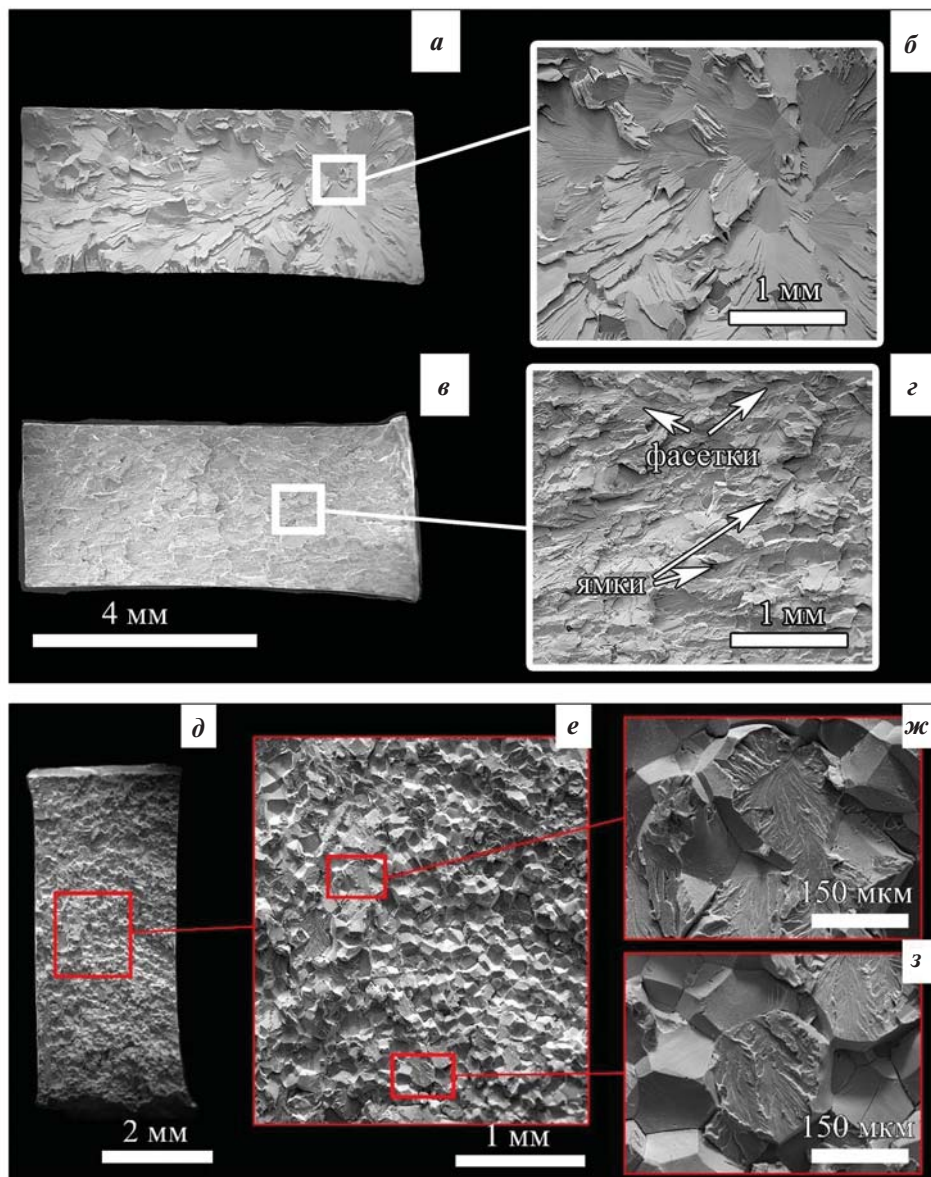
Поверхности разрушения образцов после испытаний на растяжение: общий вид и микростроение изломов сварного соединения (а, б), основного металла (в, г) и сварного соединения после термообработки (д–з)
